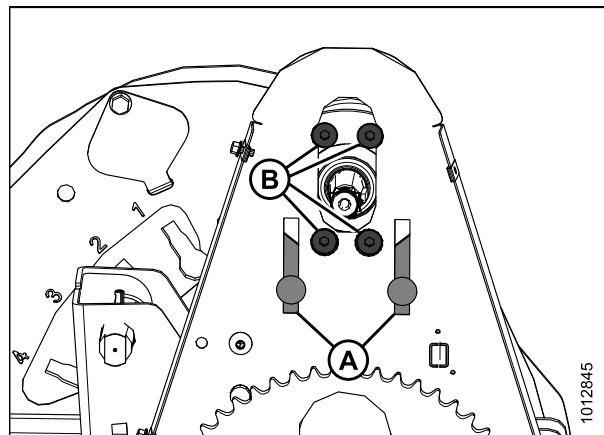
Befestigungsbohrungen des Haspelantriebsmotors
